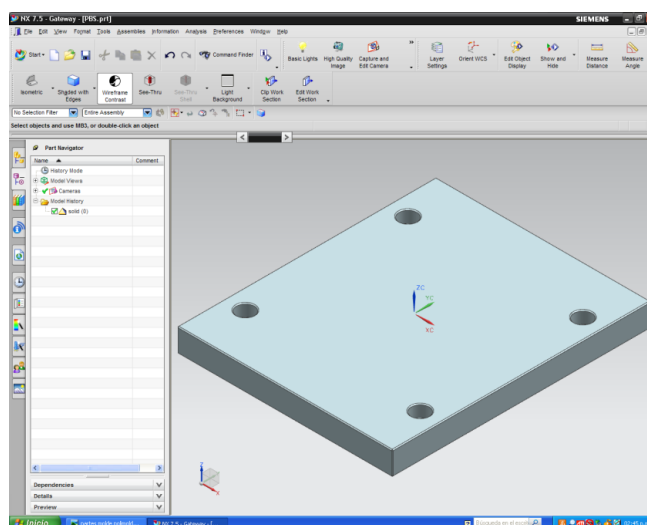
Placa frontal de sujeción PBS vista isométrica
